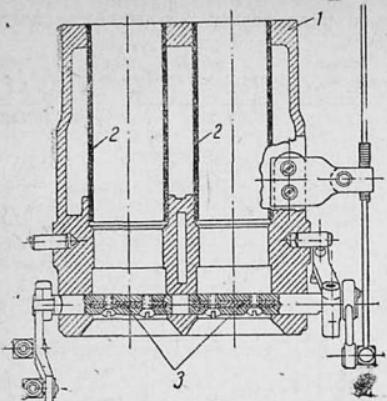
Подогреватель: 1—корпус; 2—патрубки; 3—дроссельные заслонки.
